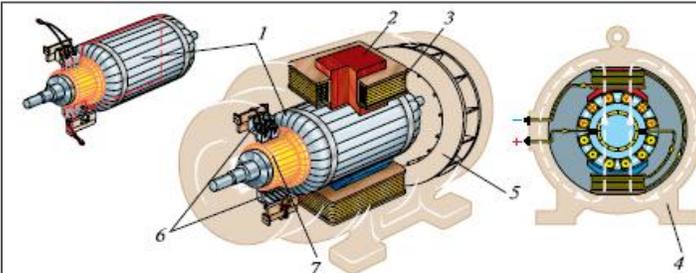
Схема коллекторного двигателя: 1 — якорь; 2 — сердечник полюса; 3 — обмотка полюса; 4 — статор; 5 — вентилятор; 6 — щётки; 7 — коллектор
